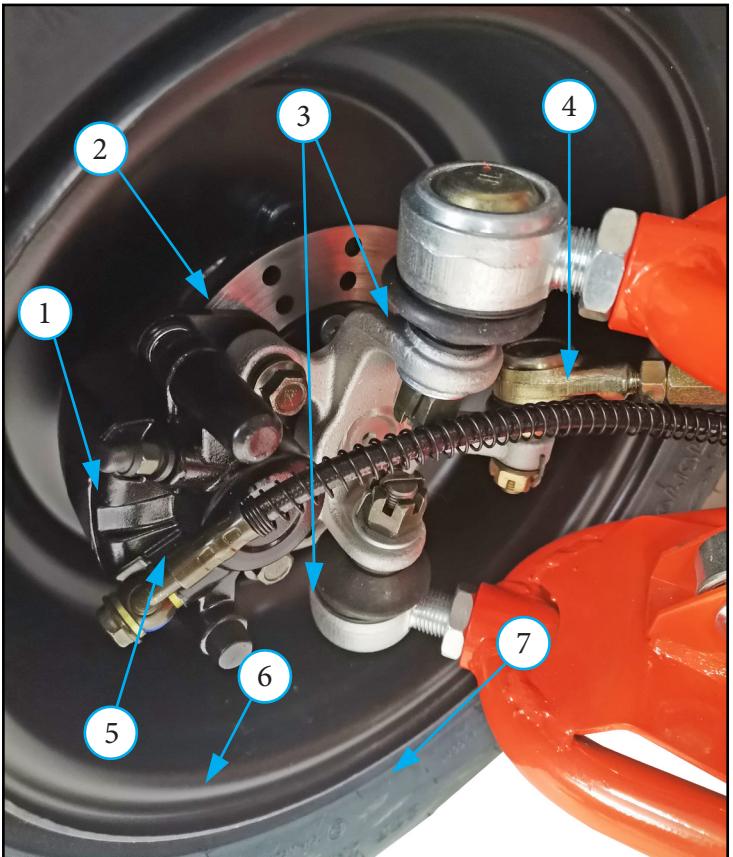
Узел поворотного кулака: 1 – передний тормозной суппорт; 2 – передний тормозной диск; 3 – шаровая опора передняя; 4 – наконечник рулевой тяги; 5 – тормозной шланг; 6 – ступица колеса; 7 – шина колеса
